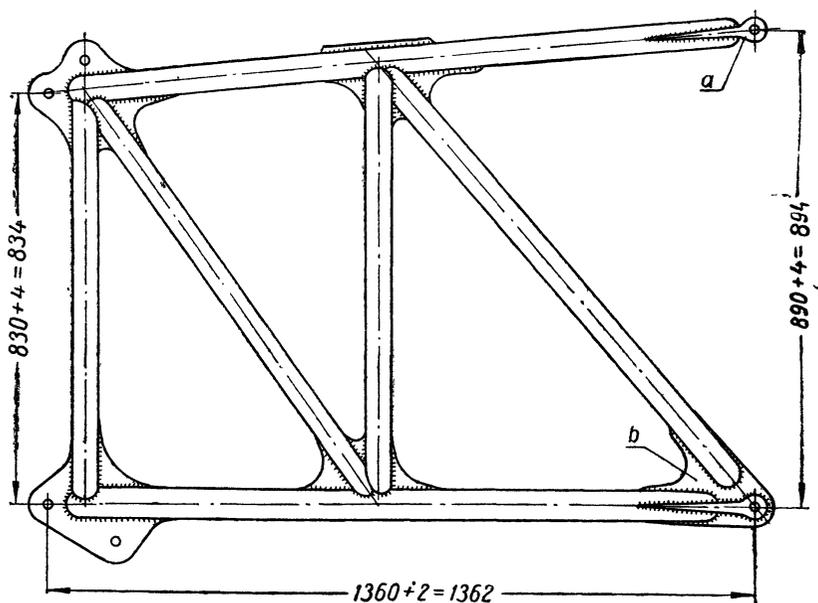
Припуски на усадку от сварки станины мотора.
